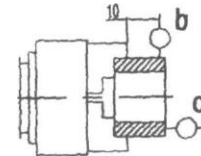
Токарный патрон с креплением заготовки за внешнюю поверхность с обратными кулачками
